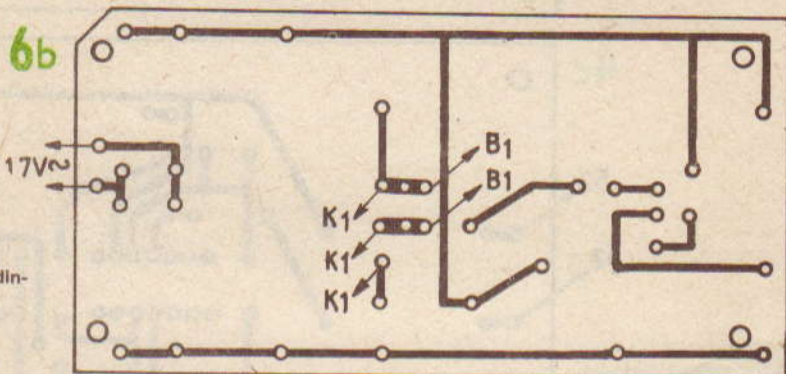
(b) Placa văzută din spate cablajul imprimat.
